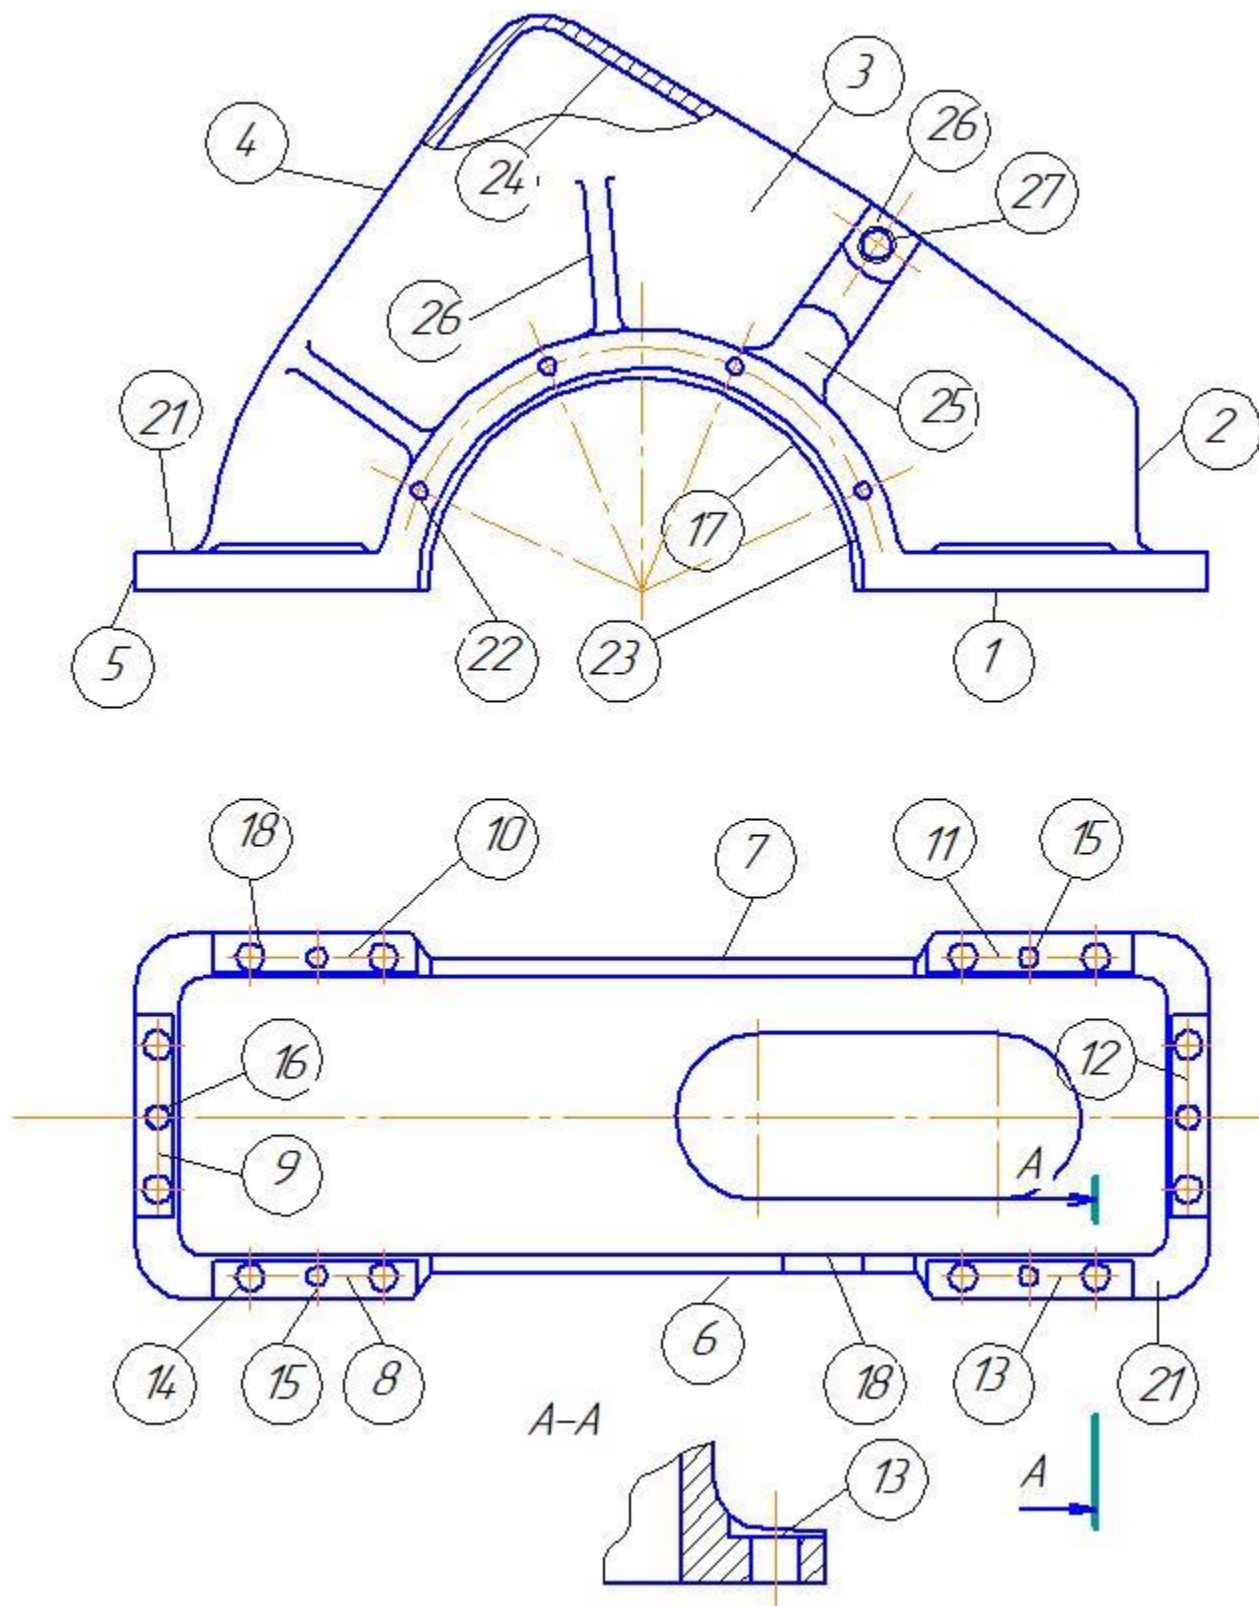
Ескіз деталі "Корпус нижній" з номерами поверхонь
